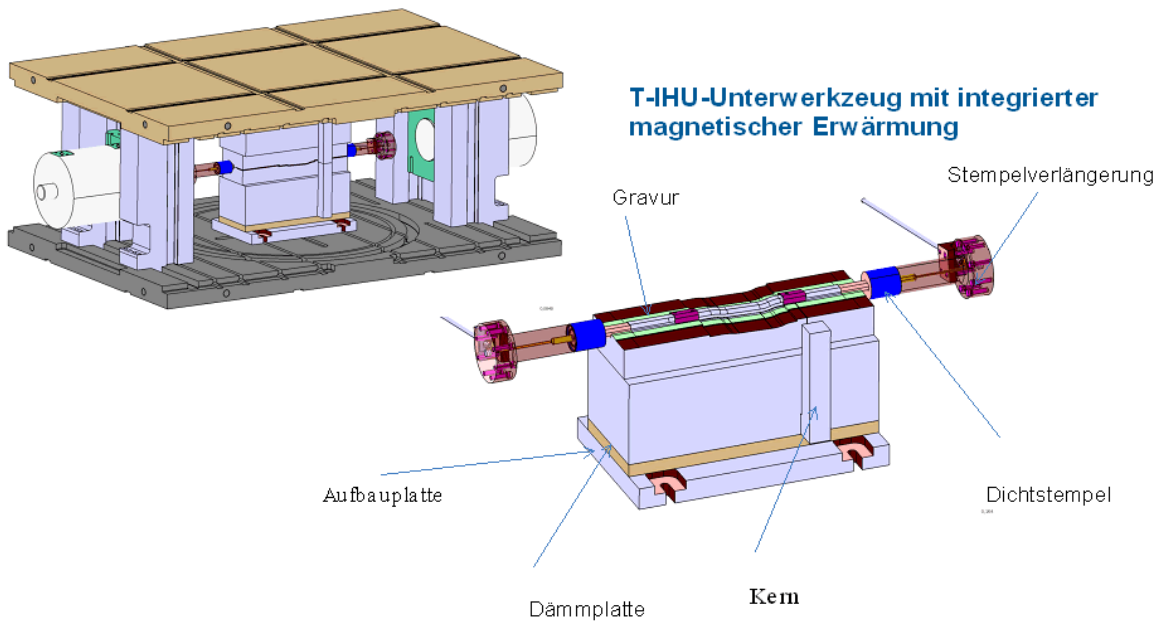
Konzipierung des T-IHU-Gesamtwerkzeuges inkl. Grundgestell (links) und der Integration der lokalen magnetischen Bauteilerwärmung ins T-IHU-Werkzeug (rechts) und konstruktive Ausführung
